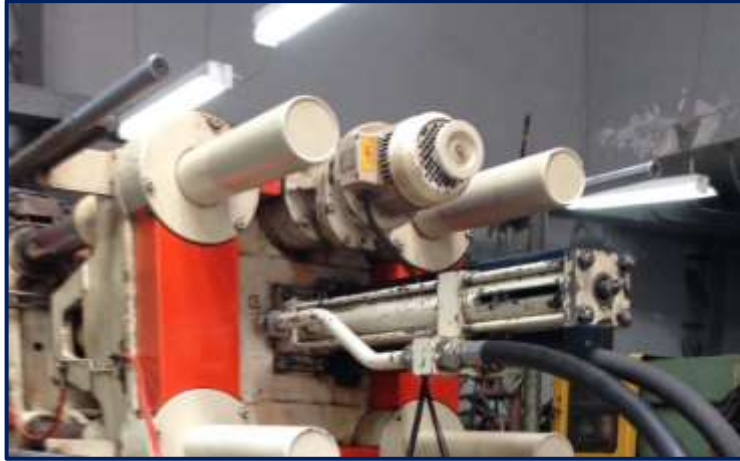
Cilindro doble efecto para la el cierre del molde en el equipo MIR de la empresa Printecsa.
